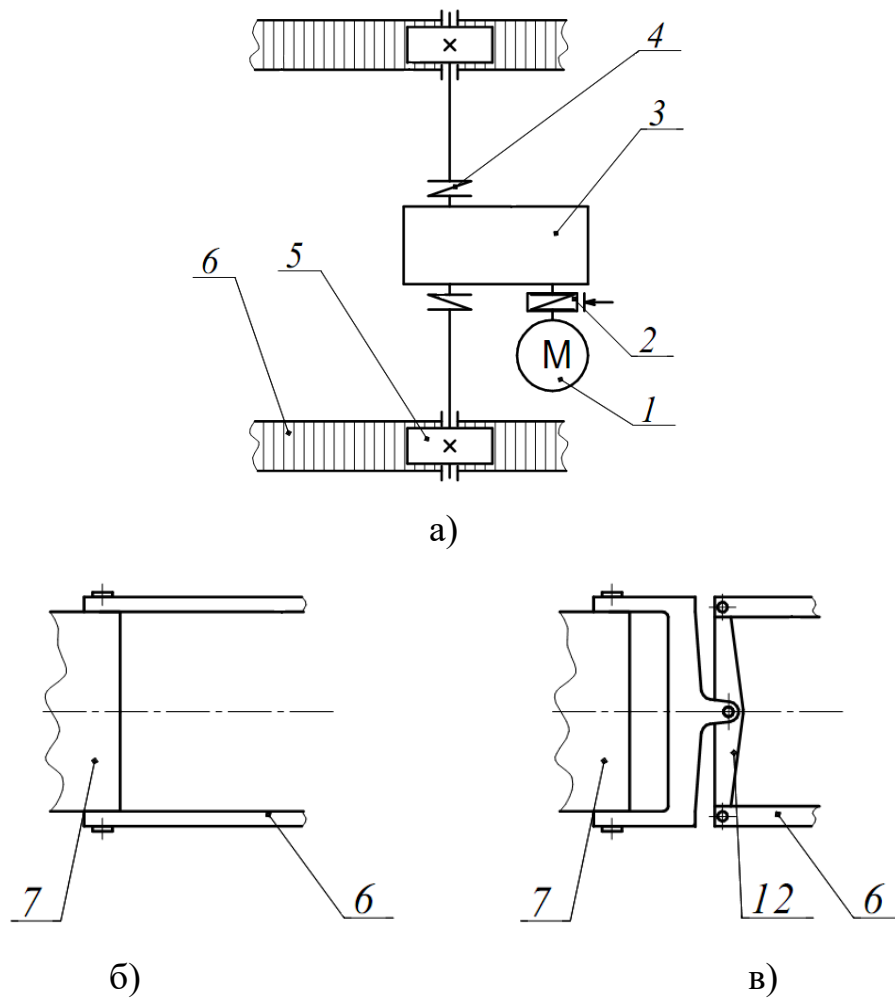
Схема механізму зміни вильоту з роздвоєною рейковою передачею: а) кінематична схема приводу; б) схема приєднання рейок безпосередньо до стріли; в) схема приєднання рейок за допомогою балансирного пристрою.
